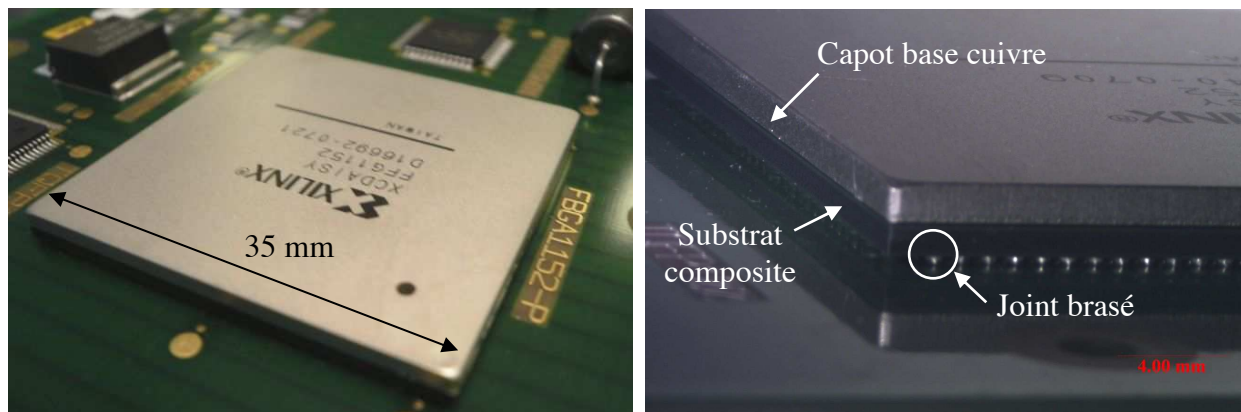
Vue d'ensemble d'un composant FBGA1152 assemblé
